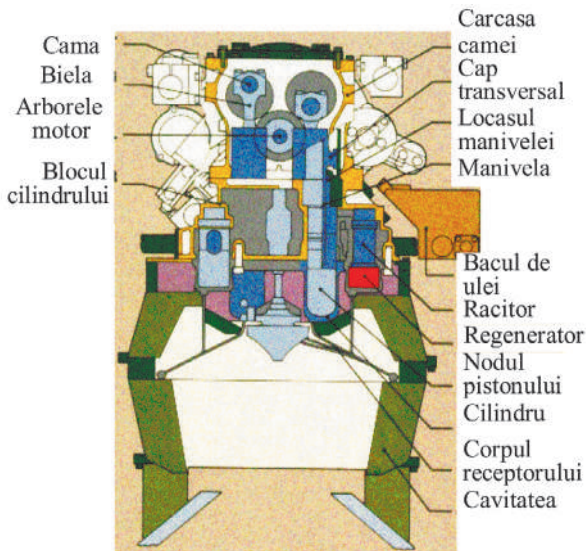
Receptorul de căldură încorporat în motorul Stirling.
